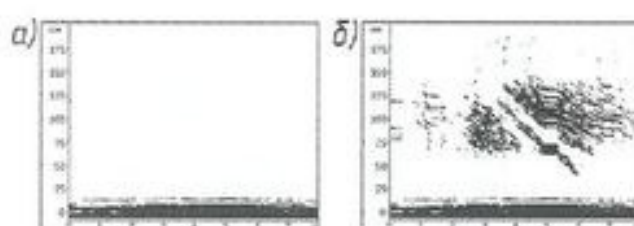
Фрагмент протокола бездефектного сварного стыка:
